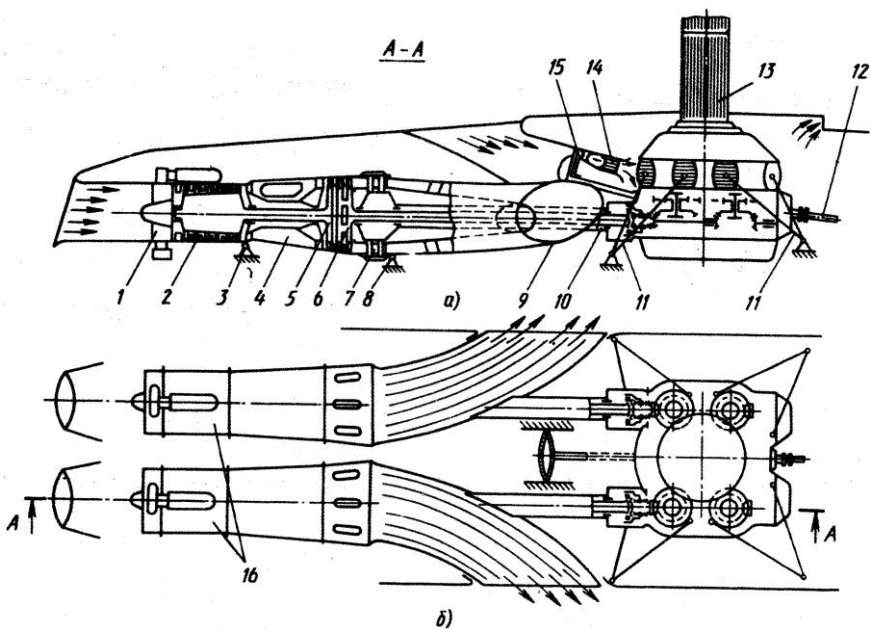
Силовая установка вертолета, работающая на один главный редуктор:
